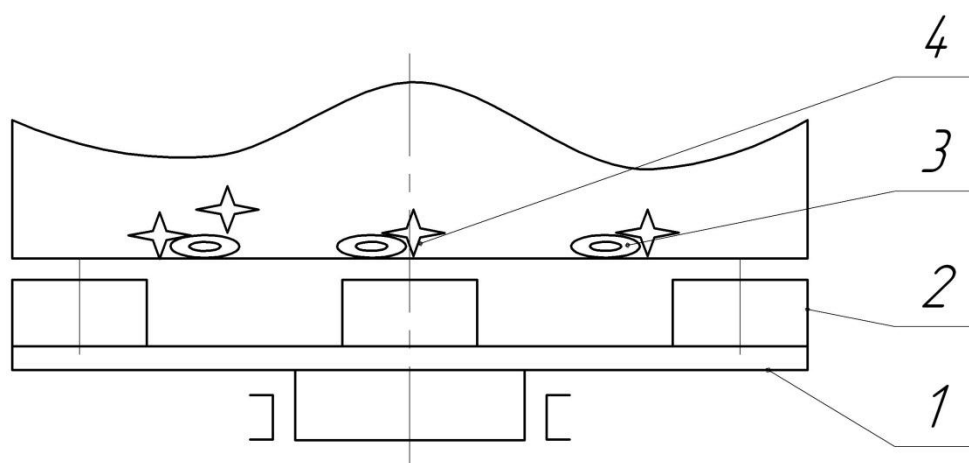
Схема магнитно-абразивной обработки деталей сложной формы из немагнитных материалов:
